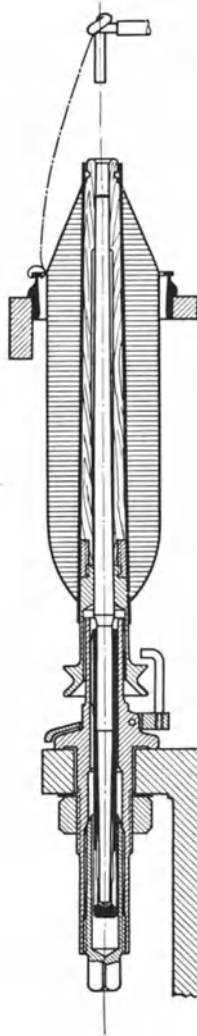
Flexible Spindel mit Gleitlager für Warpcops (Deutsche Spinnereimaschinenbau A.-G., Ingolstadt).
